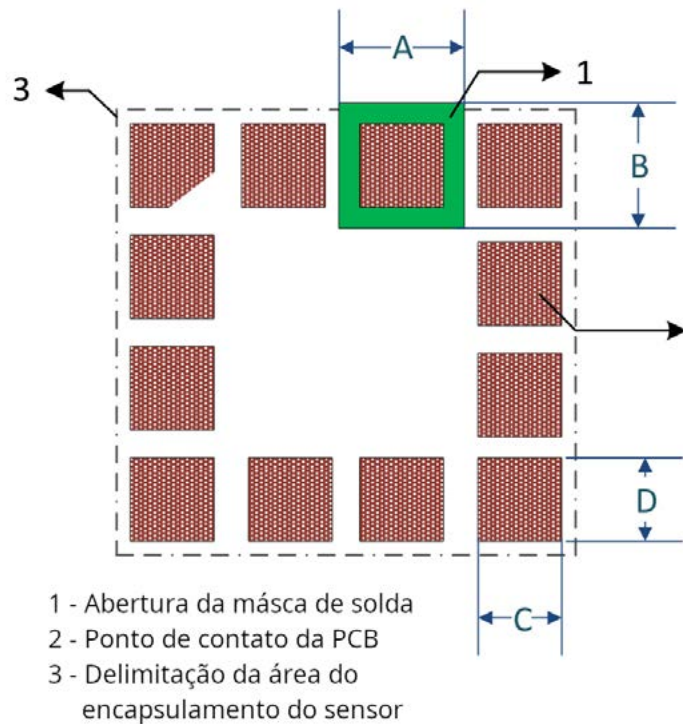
Detalhes e recomendações da geometria e dimensões dos pontos de contato da PCB e máscara de solda para encapsulamento LGA
